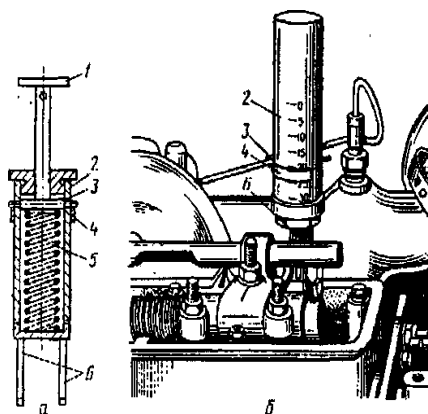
Перевірка пружності пружин клапанів газорозподілу: а - прилад для перевірки пружності; б - установка приладу на двигуні; 7 - рукоятка; 2 - корпус; 3 - натискний штифт; 4 - пасок-показчик; 5 - еталонна пружина; 6 – установка стійки
